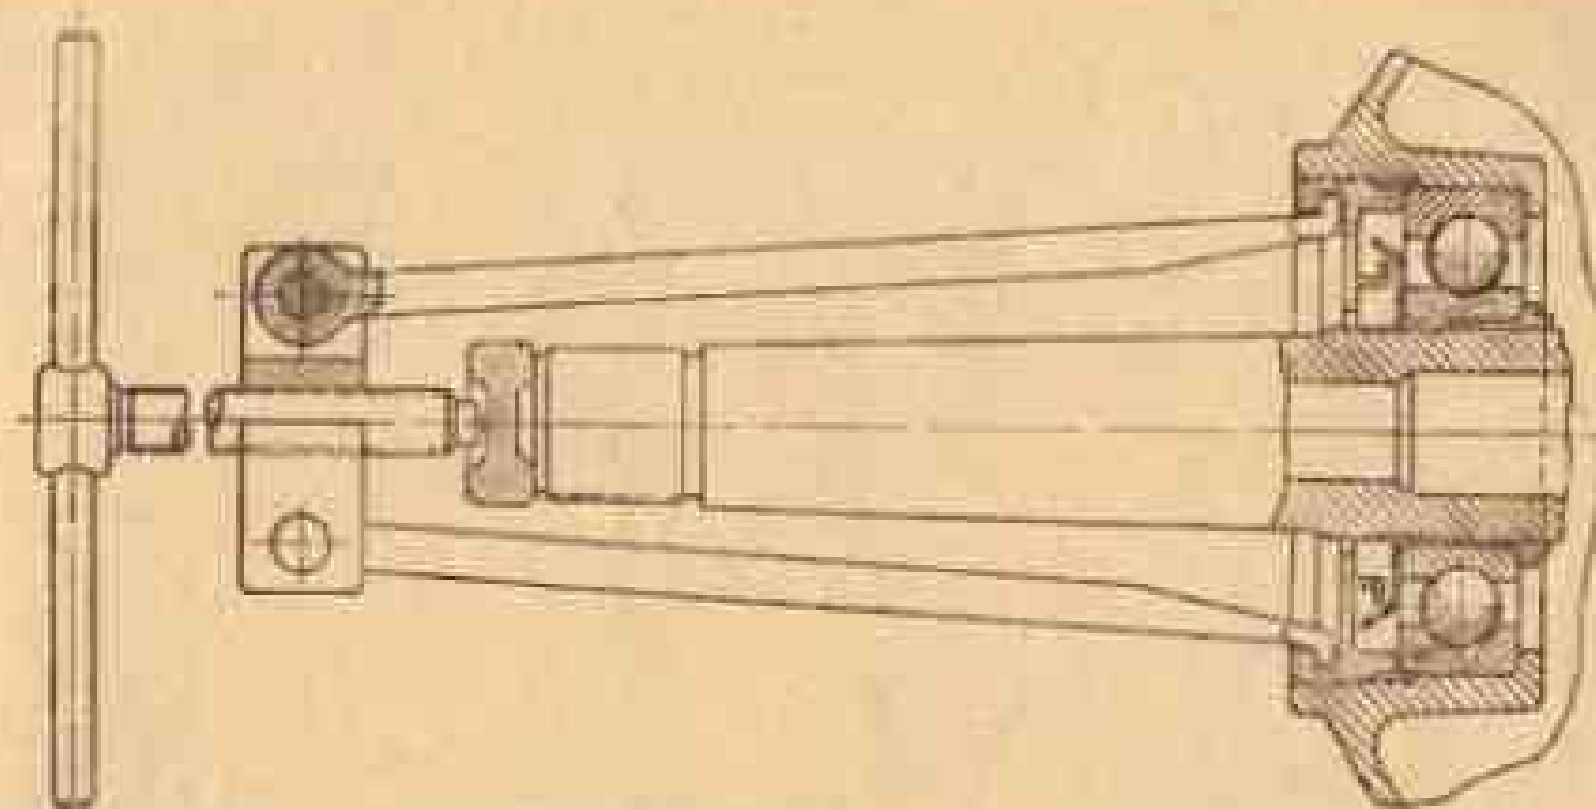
Съёмник для основной части картера и коробки газораспределения (старой конструкции).
